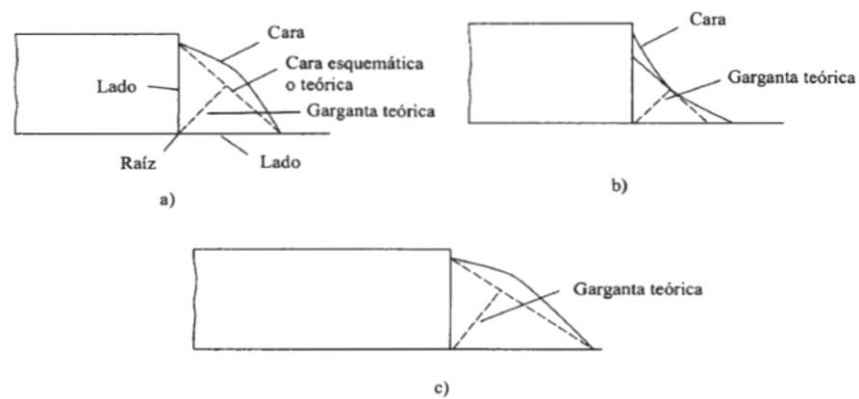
32: a) superficie convexa, b) superficie cóncava c) soldadura de filete de lados
